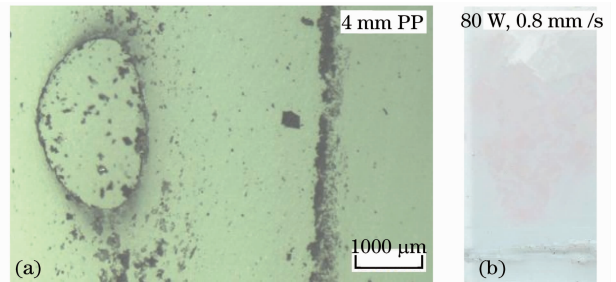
厚板的典型焊接缺陷。(a) 气孔;(b) 表面坑洼不平
